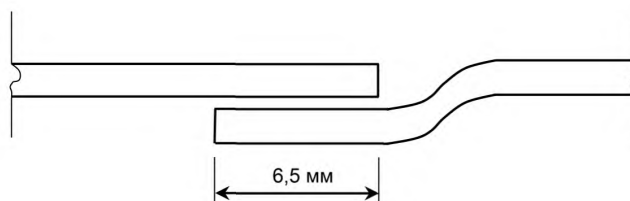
Пример прилегания дверцы к притвору корпуса
